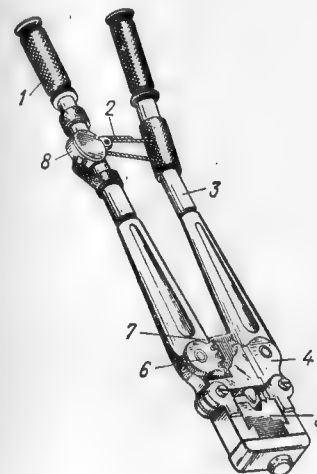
1 — ручка подвижная; 2 — трос; 3 — рычаг; 4 — корпус; 5 — матрица; 6 — сектор зубчатый; 7 — рейка с пуансоном; 8 — барабан
